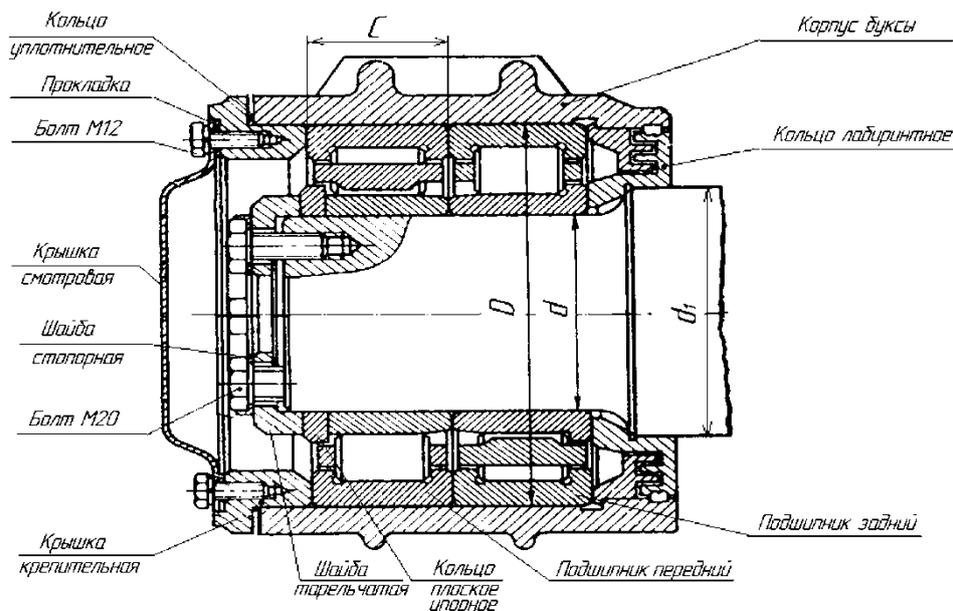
Буксовый узел с подшипниками роликовыми цилиндрическими в габаритных размерах 130 x 250 x 80 мм (тип 36-232726E2M, 36-42726E2M, 30-232726E2M, 30-42726E2M), смонтированными в корпусе буксы
